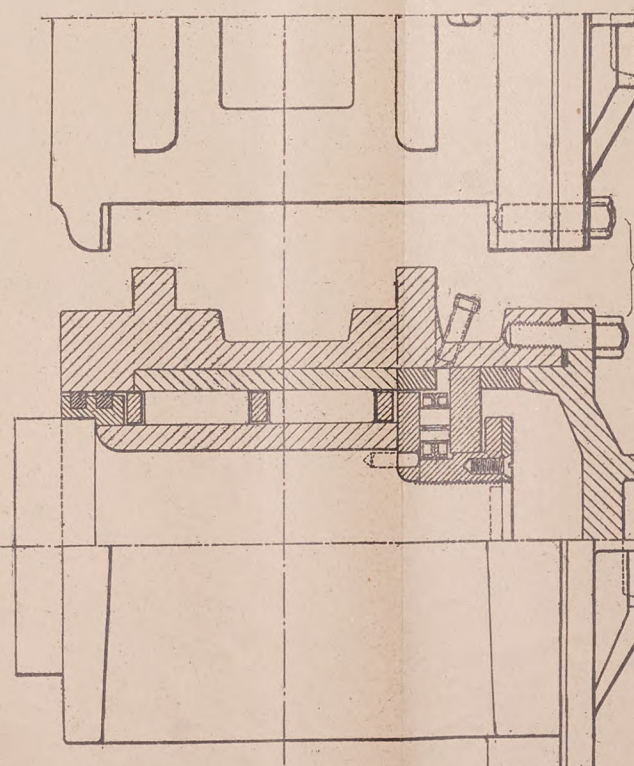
und 22. Auslaßventil für Kesselwagen.
